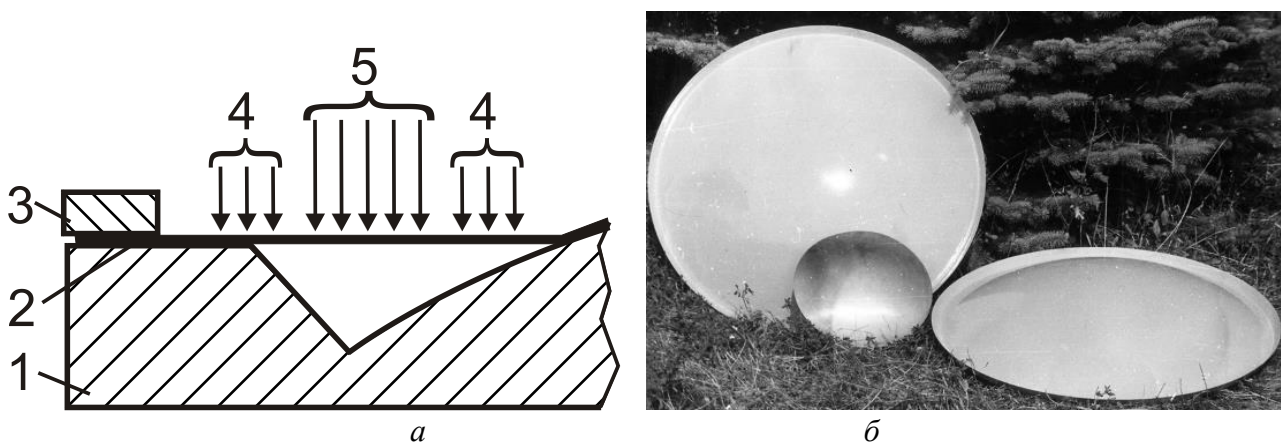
Схема фрагменту штапового налагодження дзеркала антени (1 – матриця; 2 – заготовка; 3 – притискна плита; 4 – струмені, що обтискають; 5 – основний струмінь):
